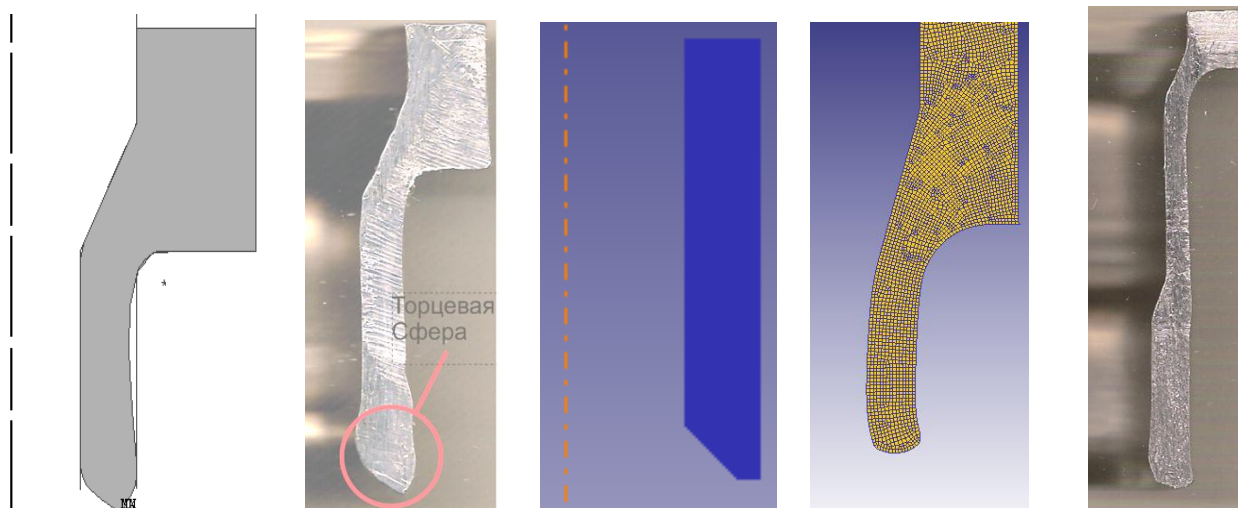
Дефект «торцева сфера», спеціально підготовлена заготовка і деталь, що отримана радіально-прямим видавлюванням
